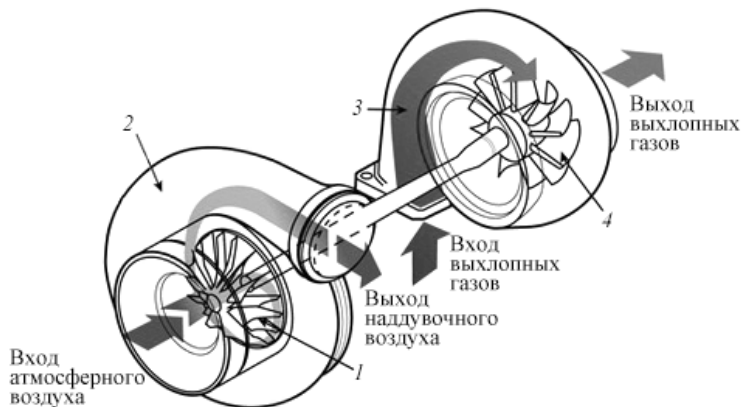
Схема работы турбокомпрессора ДВС: 1 – рабочее колесо компрессора; 2 – корпус компрессора; 3 – корпус турбины; 4 – турбинное колесо
